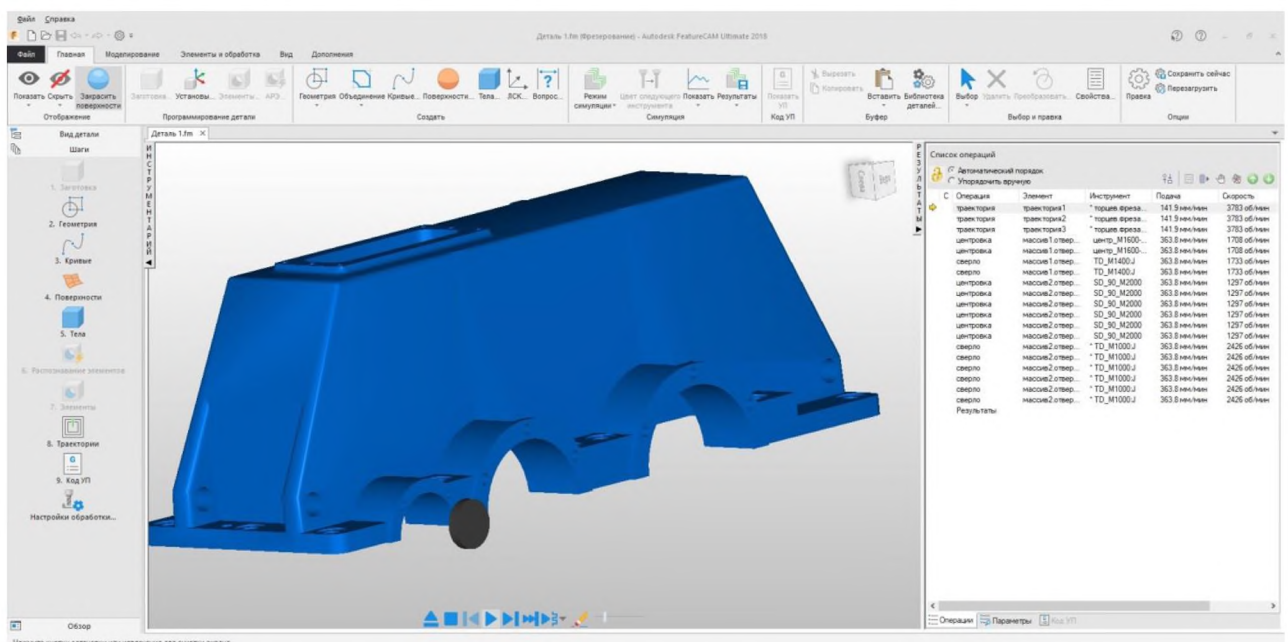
Процес обробки деталі – візуалізація фрезерування
